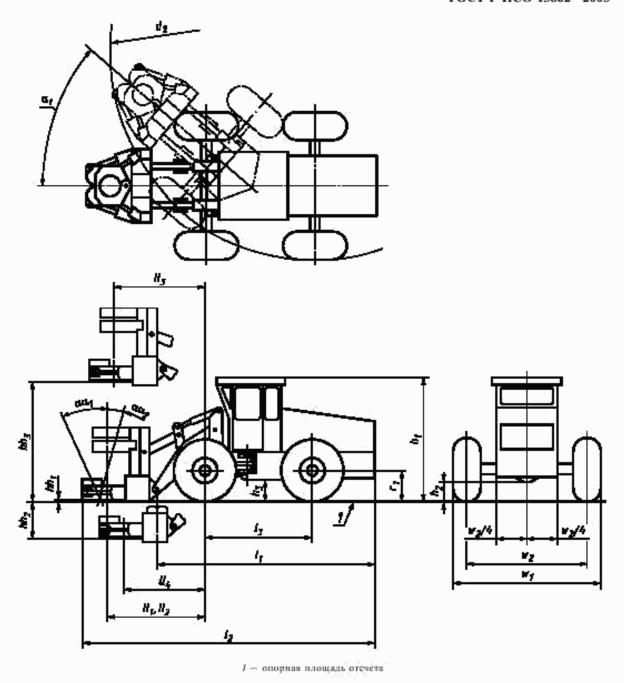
Валочно-пакетирующая машина с фронтальной навеской рабочего органа, колесный тип
